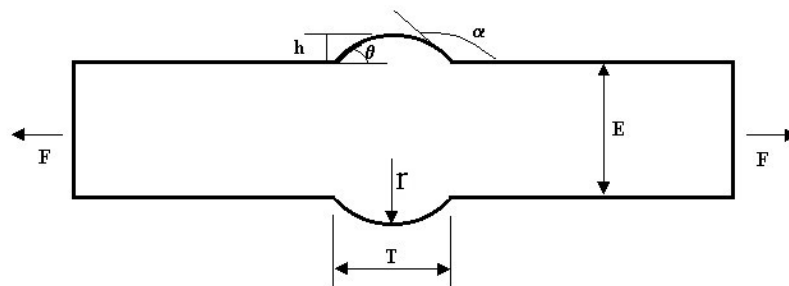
Parâmetros geométricos do cordão de solda (BRANCO 1986)
